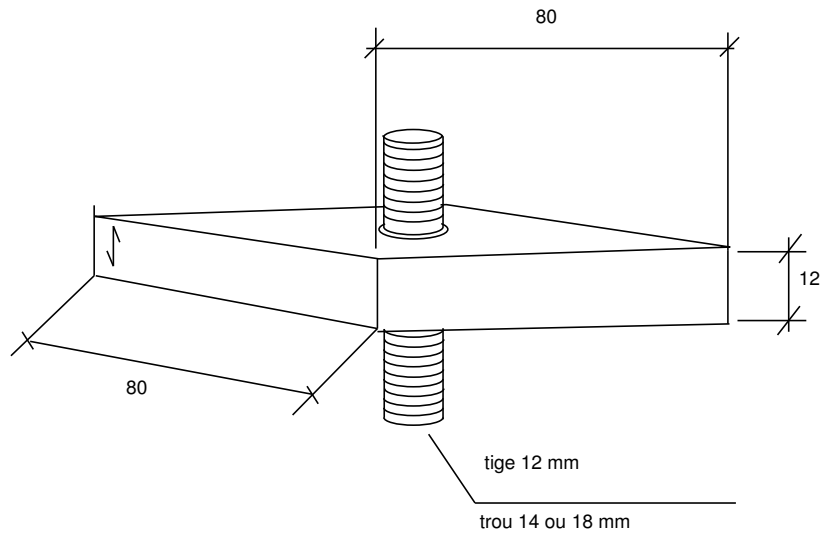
Géométrie de l'éprouvette de petites dimensions en mm
